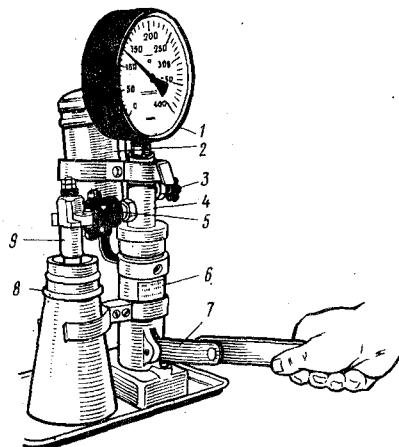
Прибор КИ-562 для проверки форсунок
